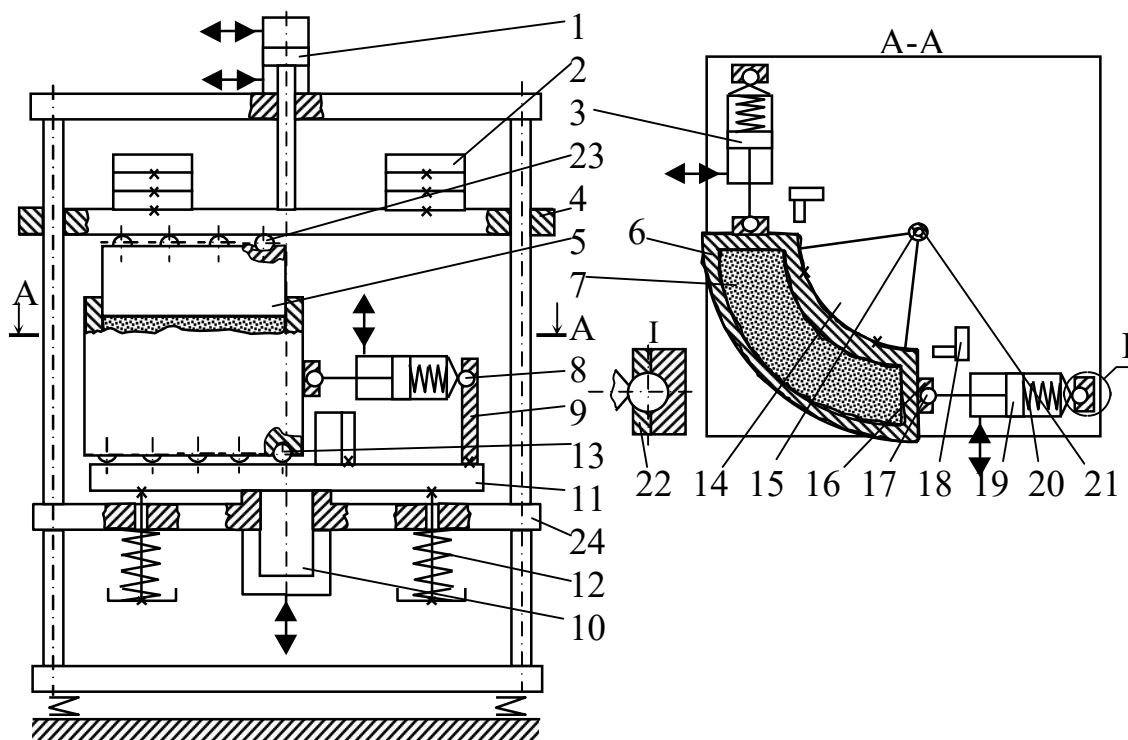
Конструктивна схема вібропреса для БКВН на базі ІВПМ з додатковим вертикальним зворотно-поворотним рухом прес-форми
